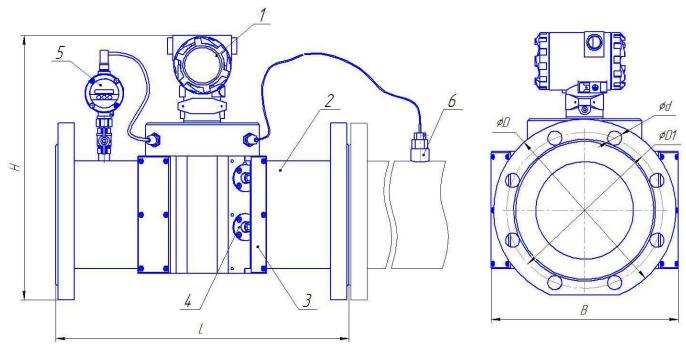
специальный корпус с установленными пъезоакустическими преобразователями;
